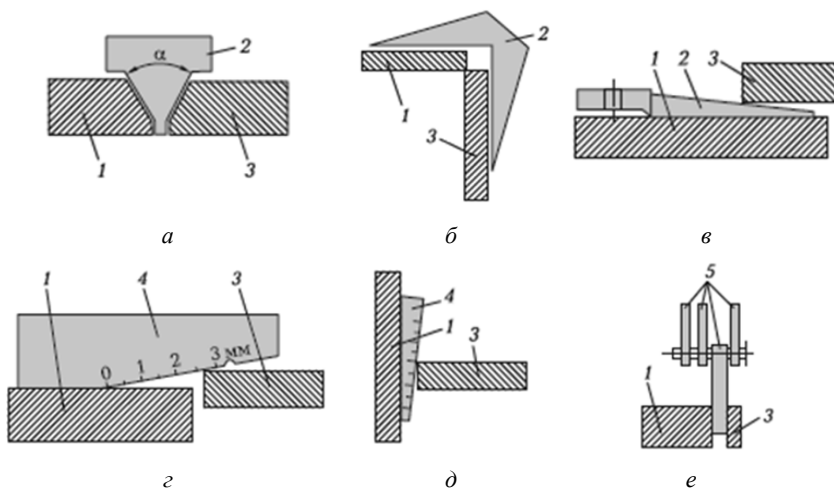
Контроль качества сборки деталей к сварке с использованием:
